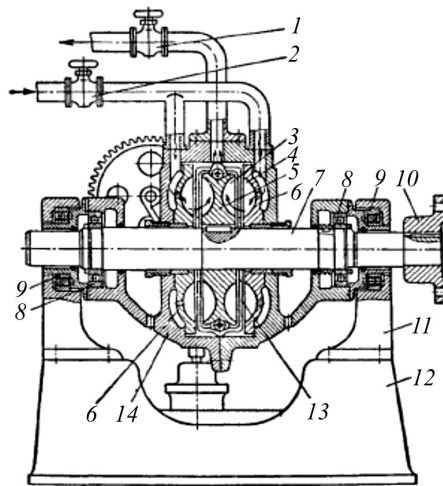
Гидравлический тормоз лопастного типа: 1 и 2 – вентили; 3 – лопатки ротора; 4 – лопатки диска статора; 5 – ротор; 6 – диск статора; 7 – вал ротора; 8 – подшипник ротора; 9 – подшипник статора; 10 – соединительная муфта; 11 – опора статора; 12 – станина; 13 – заслонки-шиберы; 14 – статор
